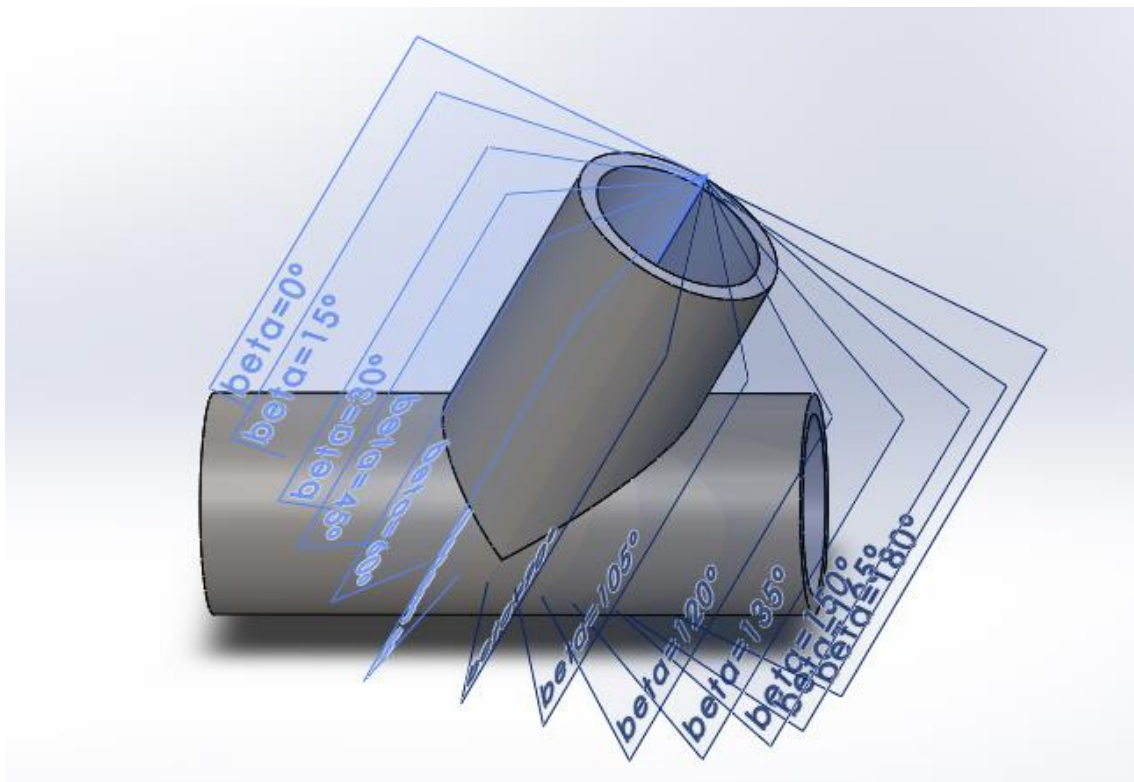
Rotación del plano de soldadura sobre el injerto (Fuente: Propia)
